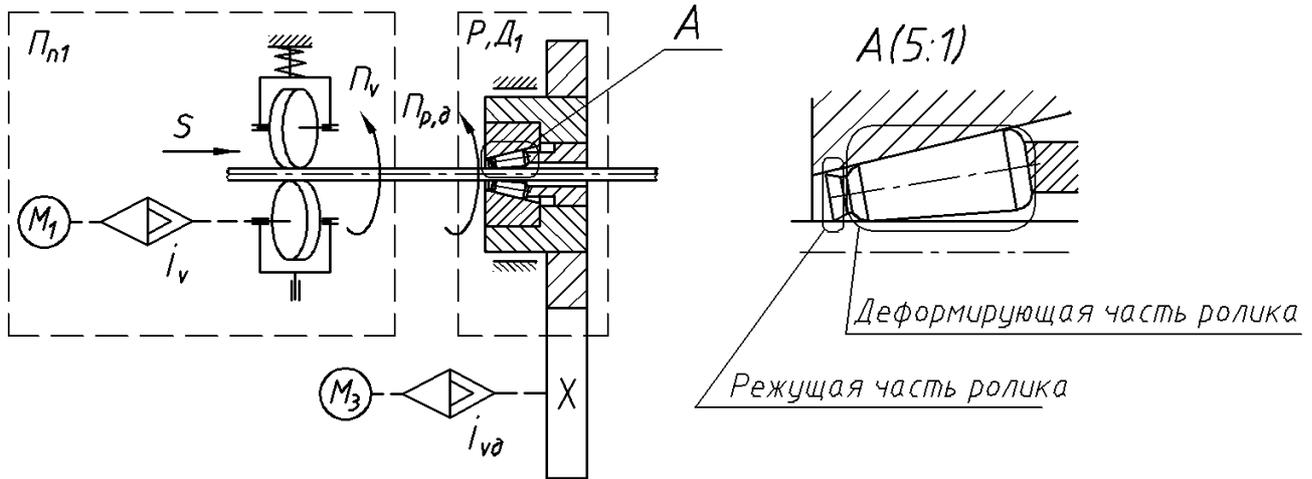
Конструктивная схема совмещенной обработки резанием и ППД роликами с подачей заготовки специальным подающим устройством и самоподачей обкатником оснащенным специальными режуще-деформирующими элементами (А)
